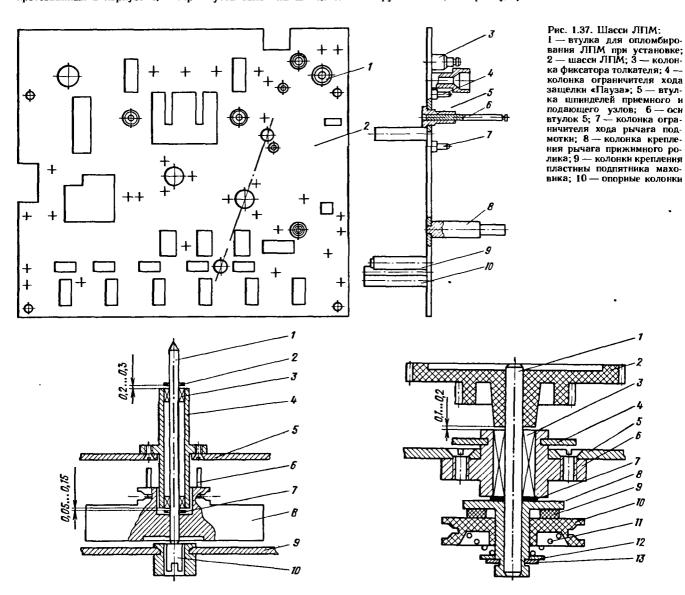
Узел ведущего вала: 1— ведущий вал; 2— щайба; 3— подшипники скольжения; 4— корпус; 5— шасси ЛПМ; 6— штыри; 7— шайба; 8— маховик; 9— втулка с пластиной; 10— подпятник
